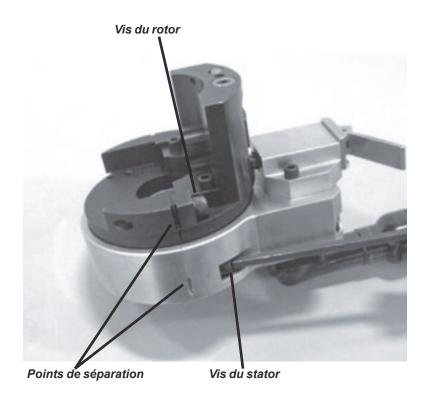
Les points de séparation de la machine peuvent être calés si nécessaire.
